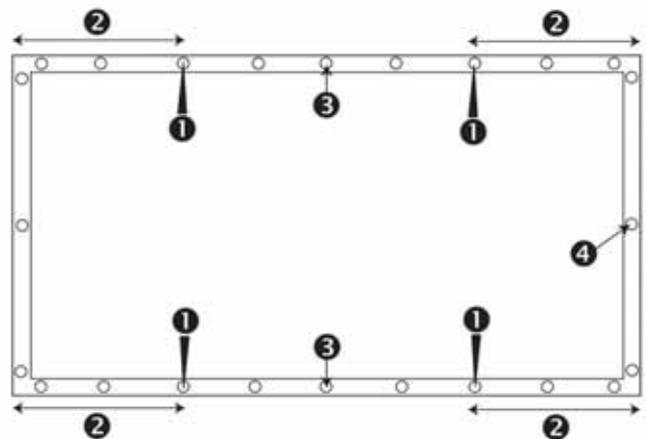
Posizione dei fori di fissaggio da utilizzare.
